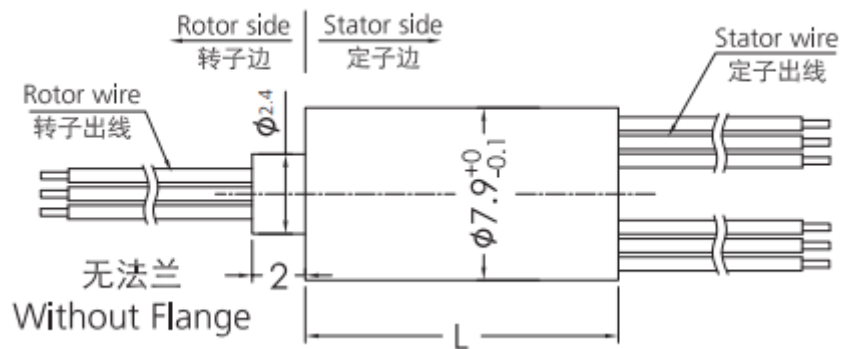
Конструкція контактного кільця Senring M079-12 [58].
